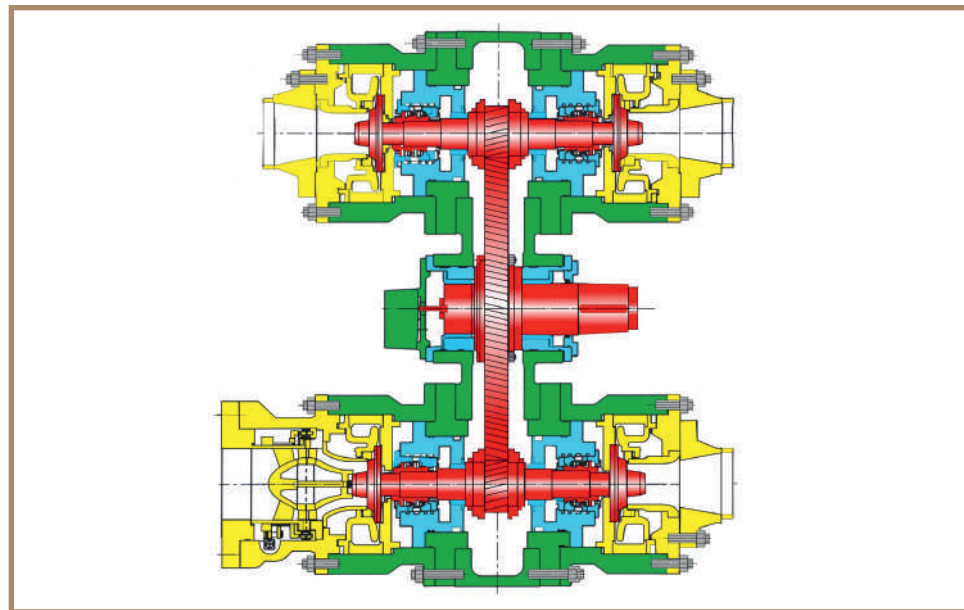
б. Многовальный центробежный компрессорный агрегат, разрез компрессора продольный
